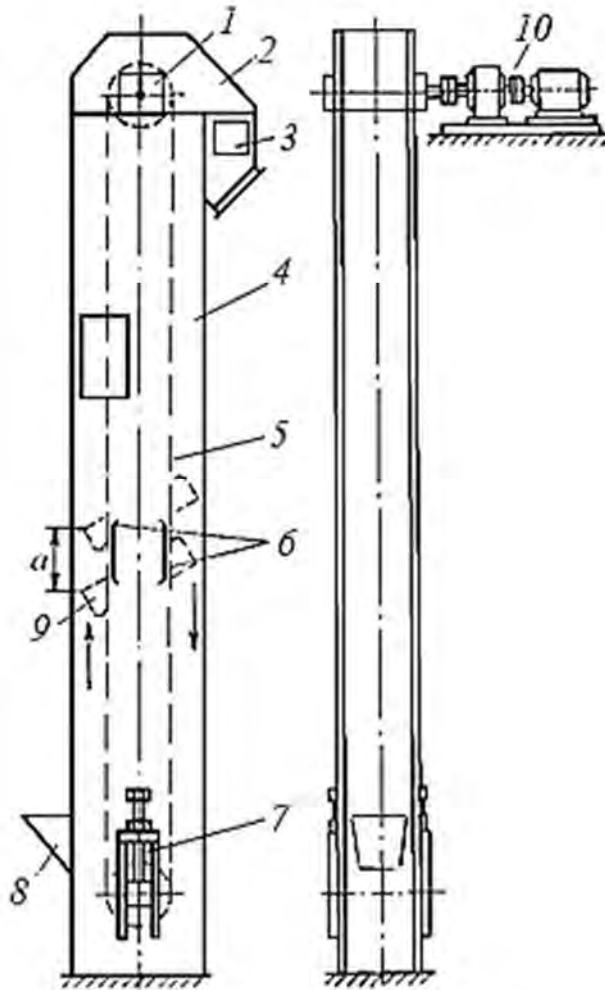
Схема ковшового элеватора: 1 – приводной барабан; 2 – разгрузочный патрубков; 3 – смотровой люк; 4 – кожух; 5 – тяговый элемент; 6 – направляющие шины; 7 – натяжное устройство; 8 – загрузочный башмак; 9 – ковш; 10 – привод
